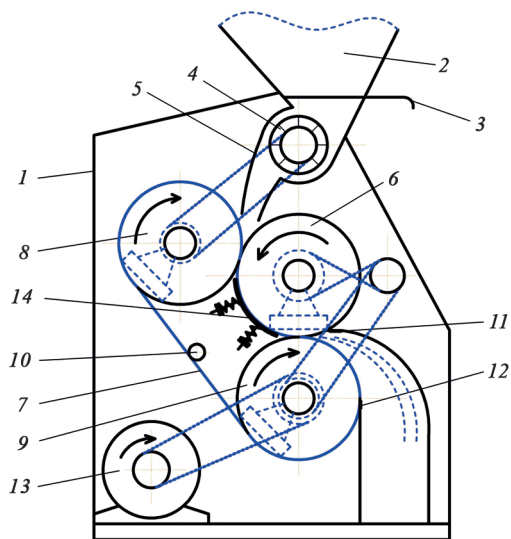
Конструкция двухступенчатой вальцово-ленточной плющилки:
